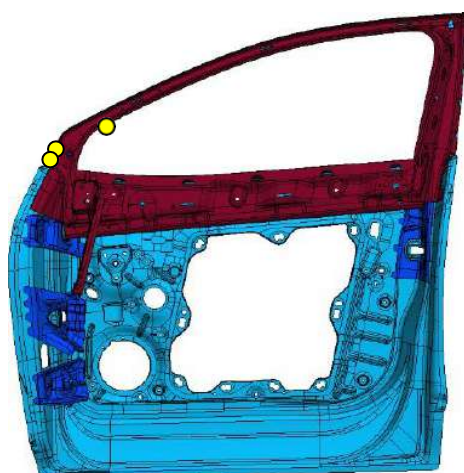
Розподіл зварювальних точок по кузову дверцят пристрою стаціонарного зварювання пристрою
